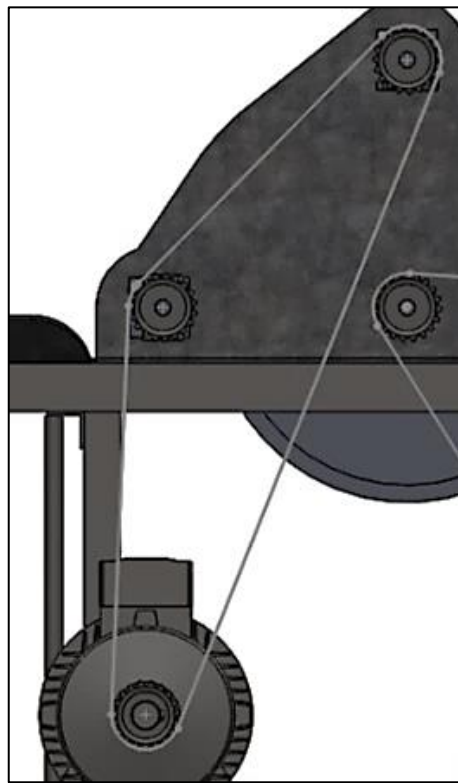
Sistema de transmisión para los rodillos cardadores
